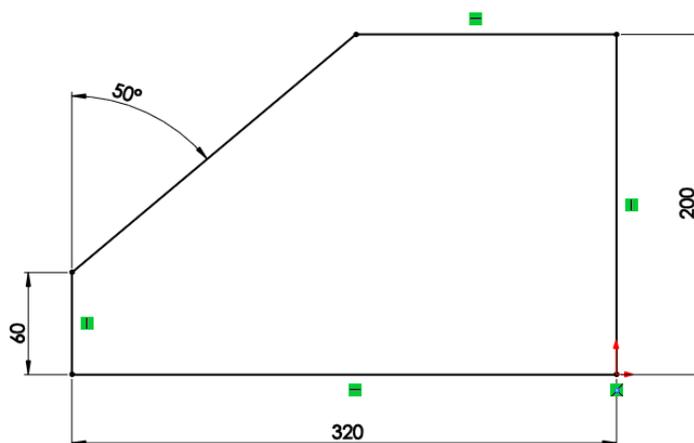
Esboço de um bloco com as dimensões totais do carrinho.
